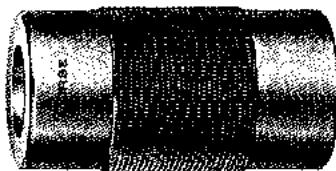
Calibre cónico de anillo (Morse Twist Drill & Machine Co.).
